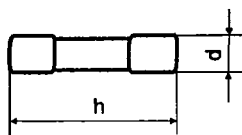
Тип корпуса быстродействующего плавкого предохранителя
